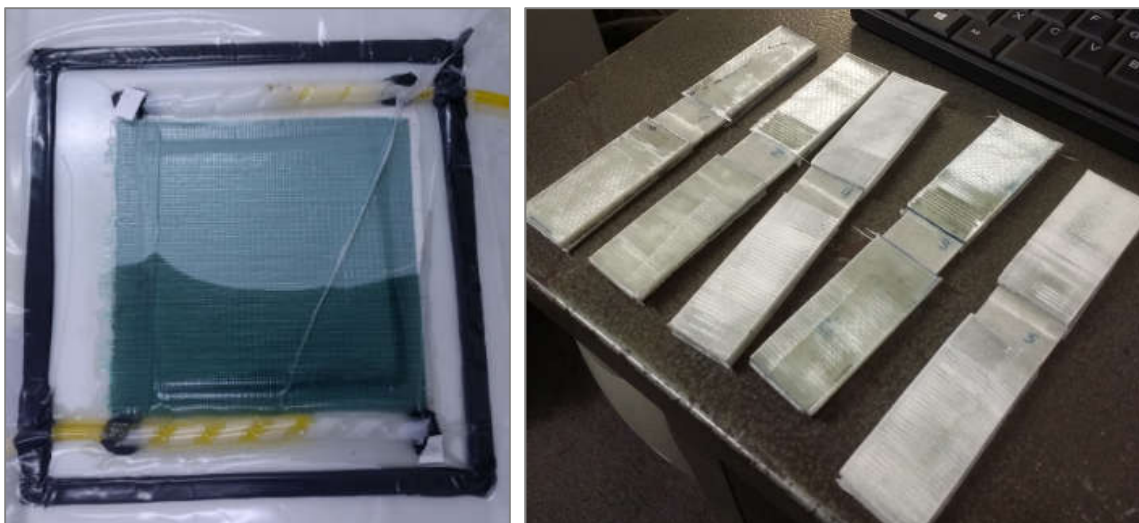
Proceso de fabricación (izquierda); Probetas fabricadas para determinación de α_0 (derecha).
